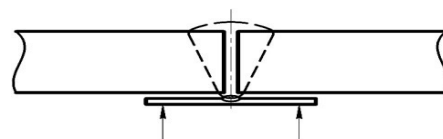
Сварка на медно-флюсовой подкладке
